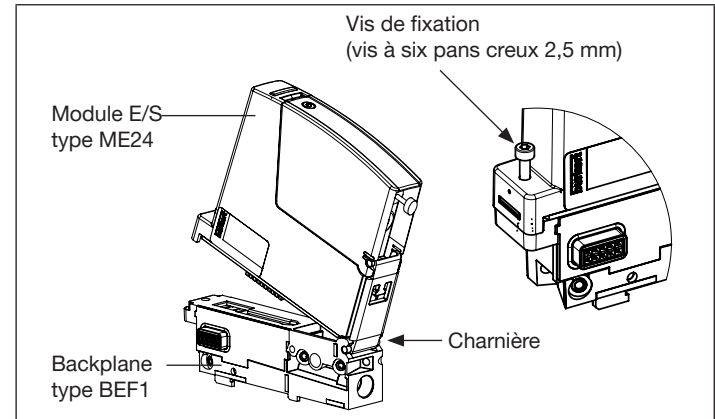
Monter le module E/S de type ME24 sur la backplane de type BEF1
